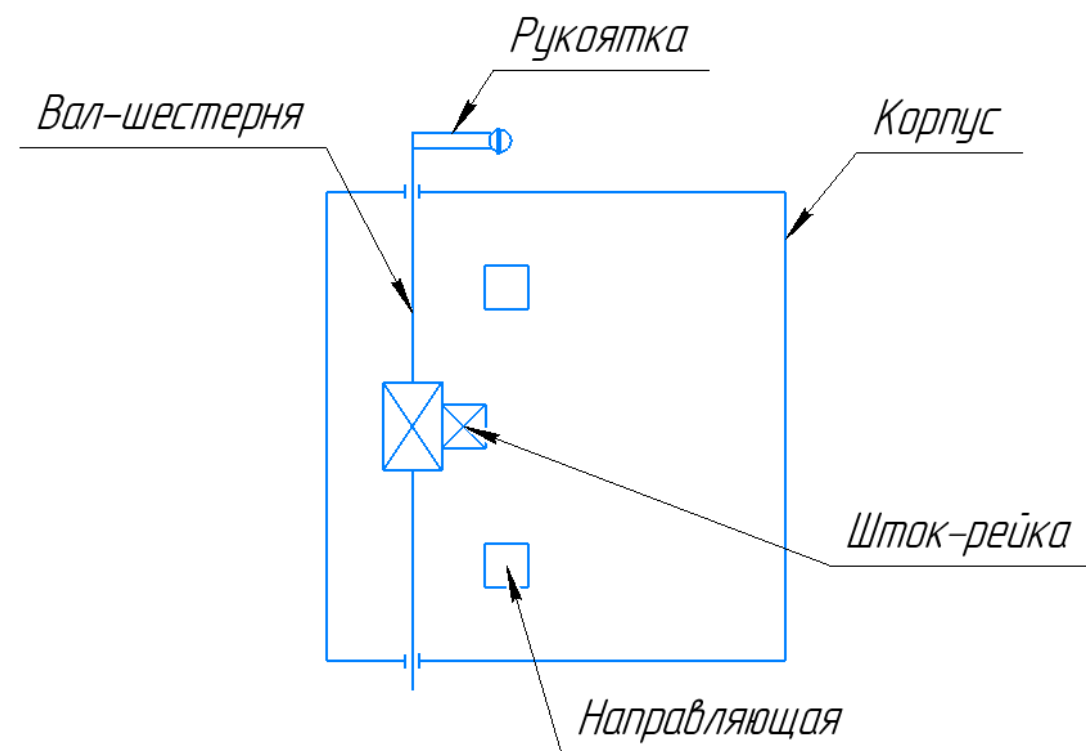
Кинематическая схема разработанного специального приспособления
